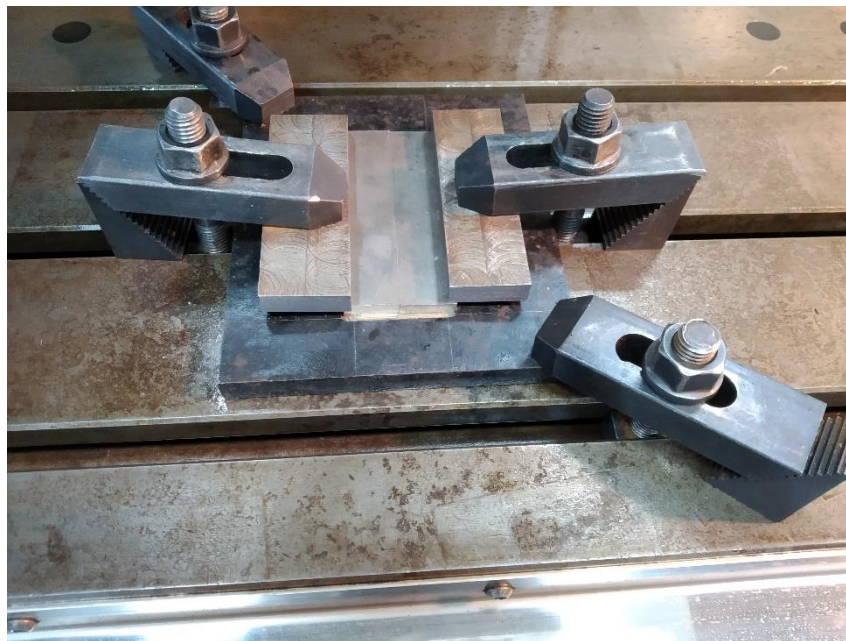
Sistema de fixação completo já com o corpo de prova preparado para o ensaio de soldagem FSW.
